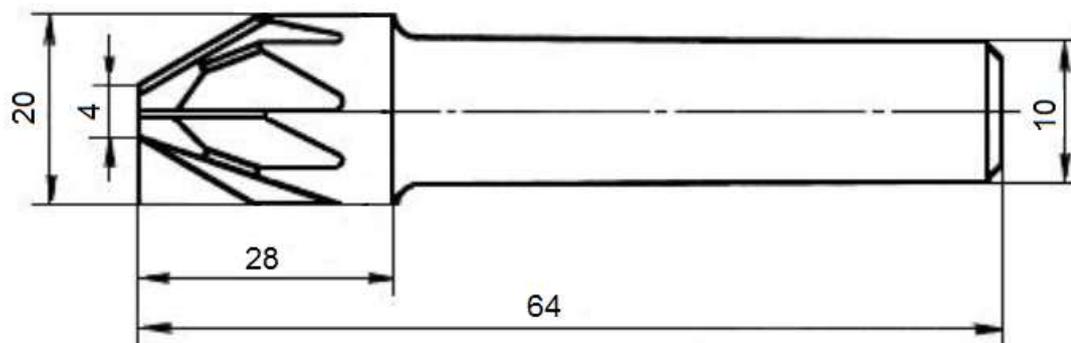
Зенковка 2353-0105 ГОСТ 14953-80
